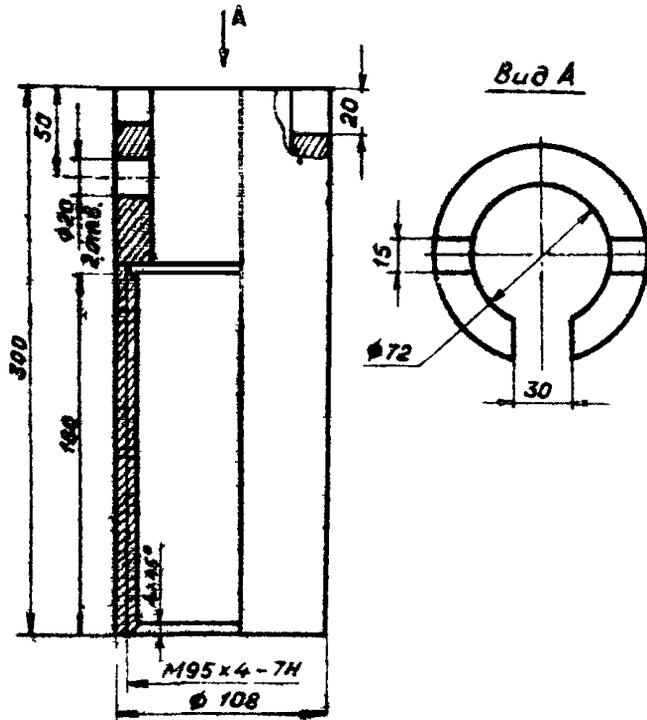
Разрезная головка для допуска заземлителя до расчетной глубины.
